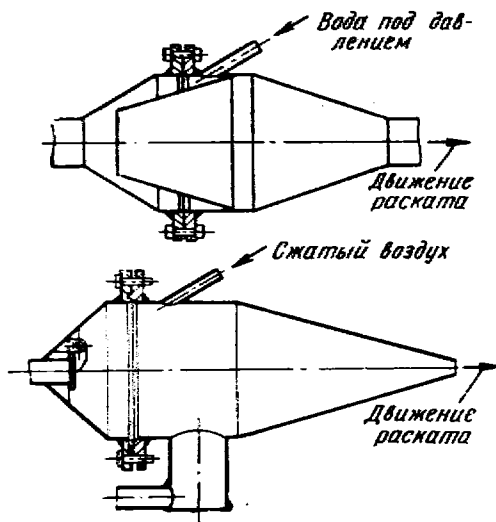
Устройства для термомеханического упрочнения сортовой стали
